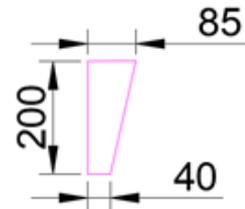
Dimensiones de las piezas utilizadas en la unión. Fuente: propia.
